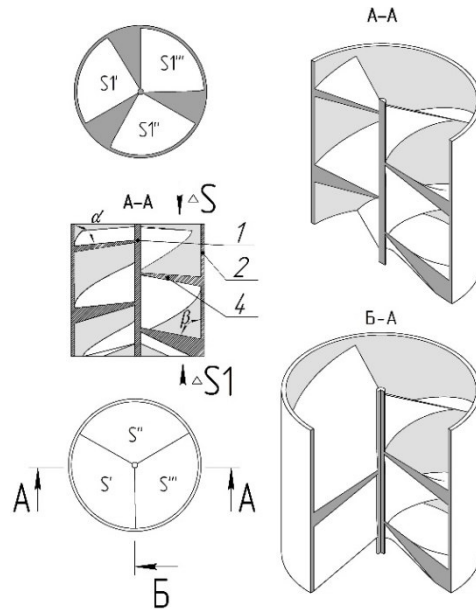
Схема турбіни зі спіралеподібними лопатями (1 – вал, 2 – порожнистий циліндричний корпус, 3 – спіралеподібна лопать)
